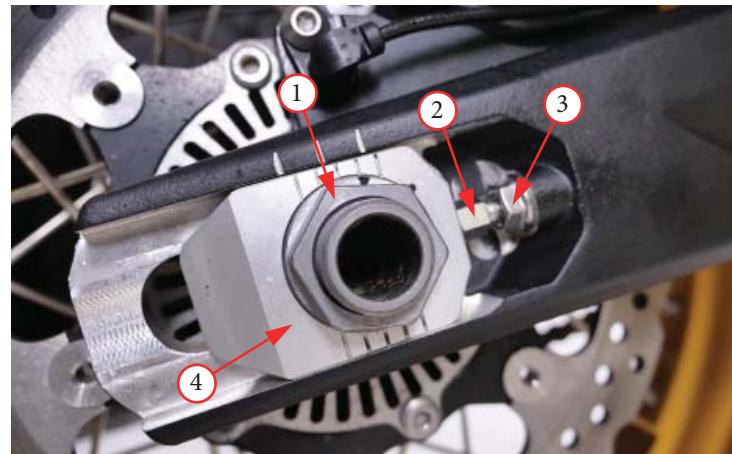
Регулировка натяжения цепи: 1 – гайка оси; 2 – регулировочный болт; 3 – стопорная гайка; 4 – кронштейн натяжителя
